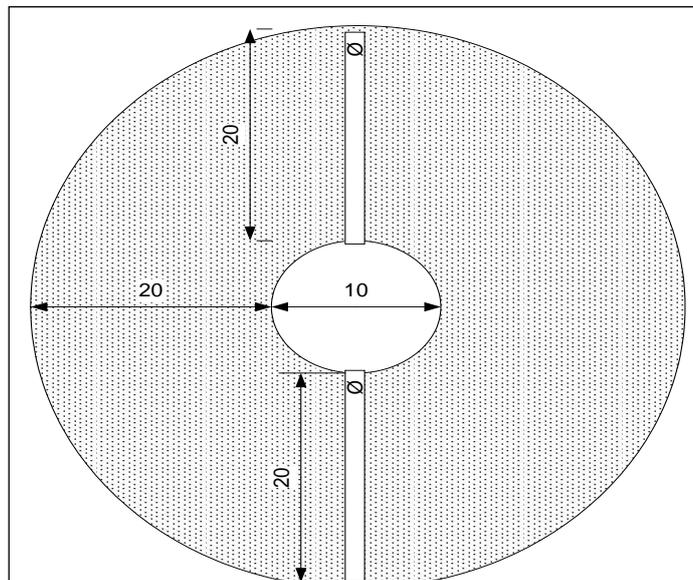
Dimensiones de la tapa para el tanque de almacenamiento 2.
